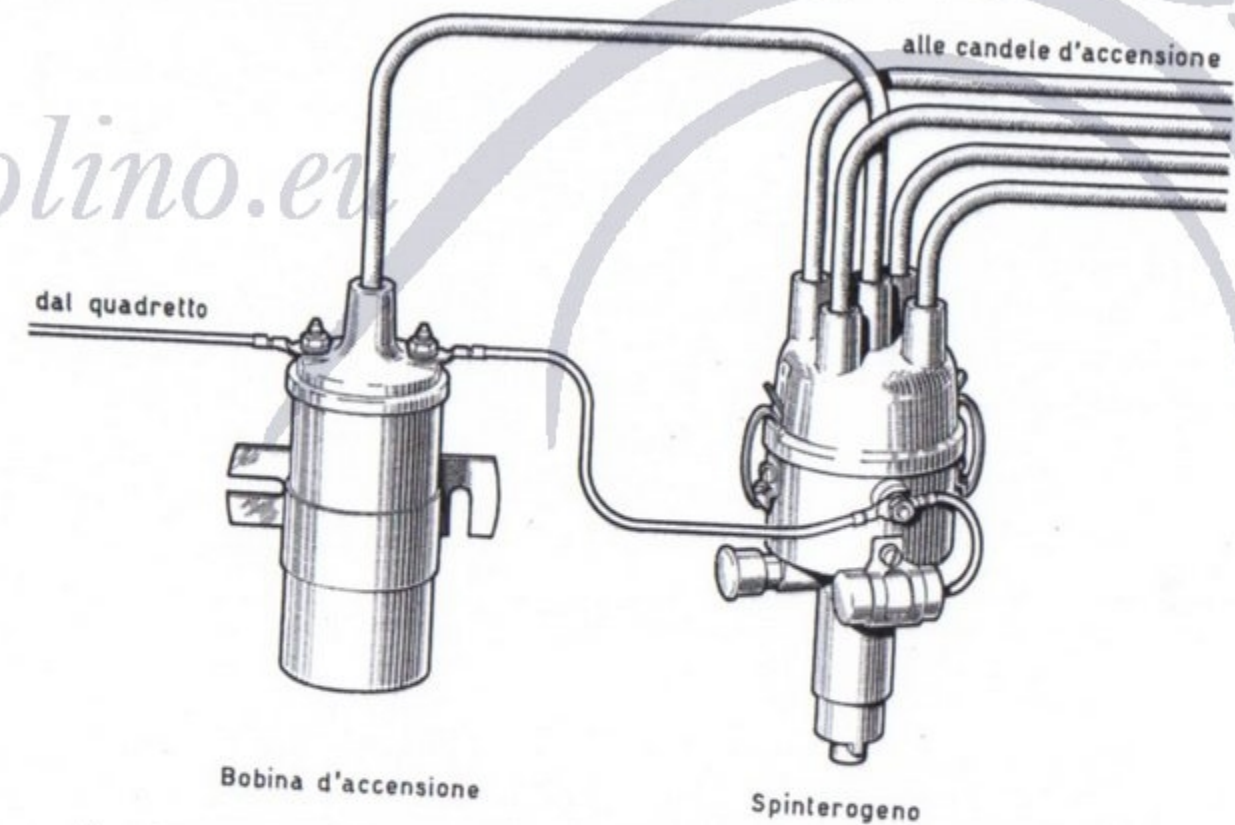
Sistema di accensione a batteria per autoveicoli con motore a quattro cilindri.
